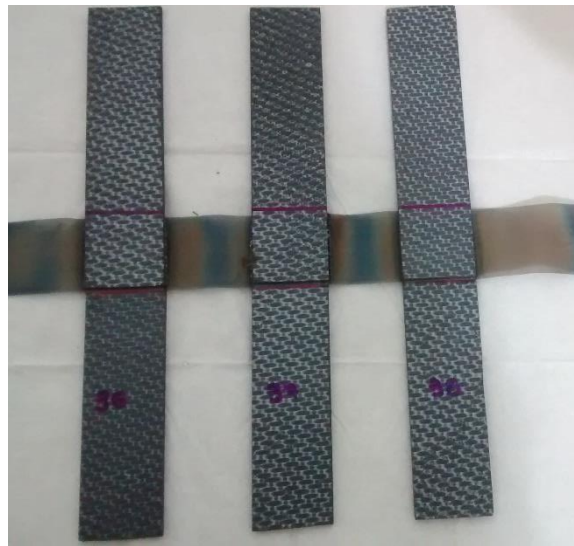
Corpos de prova para os ensaios de *Lap Shear* sendo soldados (soldadora por resistência elétrica).
